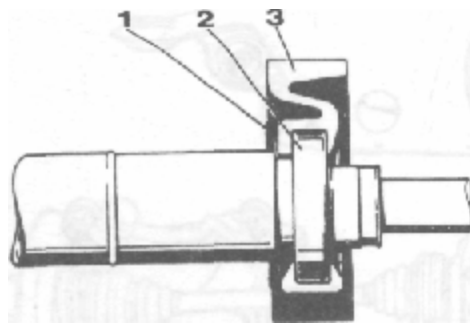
Правильная установка подшипника в резиновой опоре
